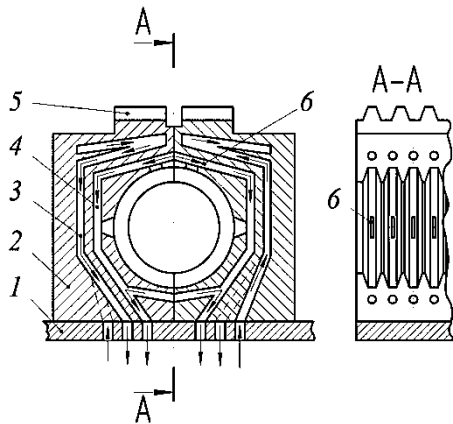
Поперечний розріз півформ гофратора з вакуумною калібруванням: 1 – плита машини; 2 – півформи; 3 – канал для охолоджувальної води; 4 – канал для вакуумування; 5 – рейки; 6 – прорізи для вакуумування формувальної поверхні
